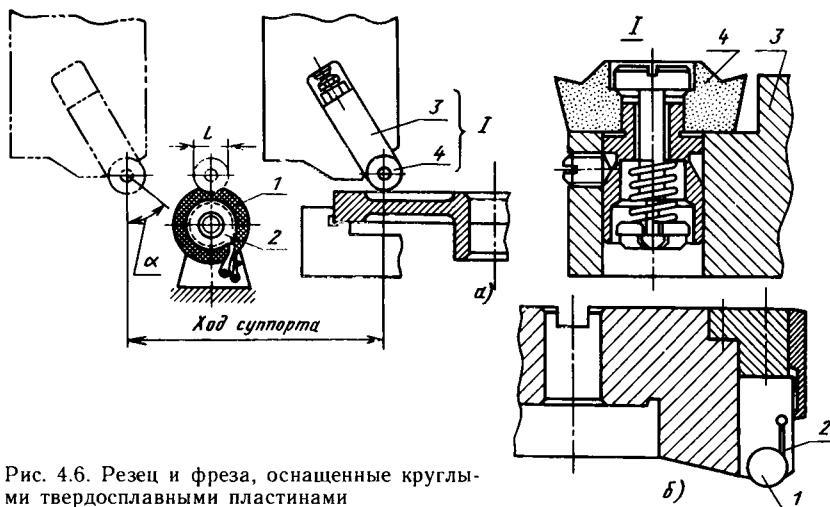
Резец и фреза, оснащенные круглыми твердосплавными пластинами
